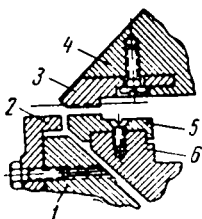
Крепление линеек на кромкогибочном станке с ручным приводом:
